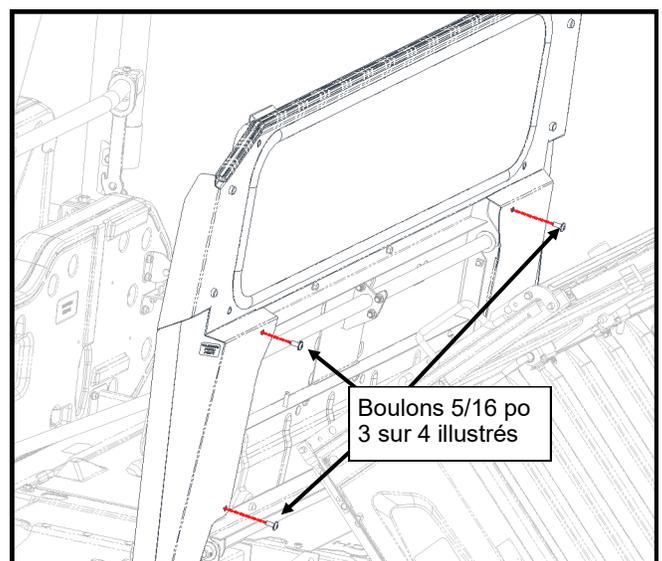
Panneau arrière inférieur sur le grillage de siège
